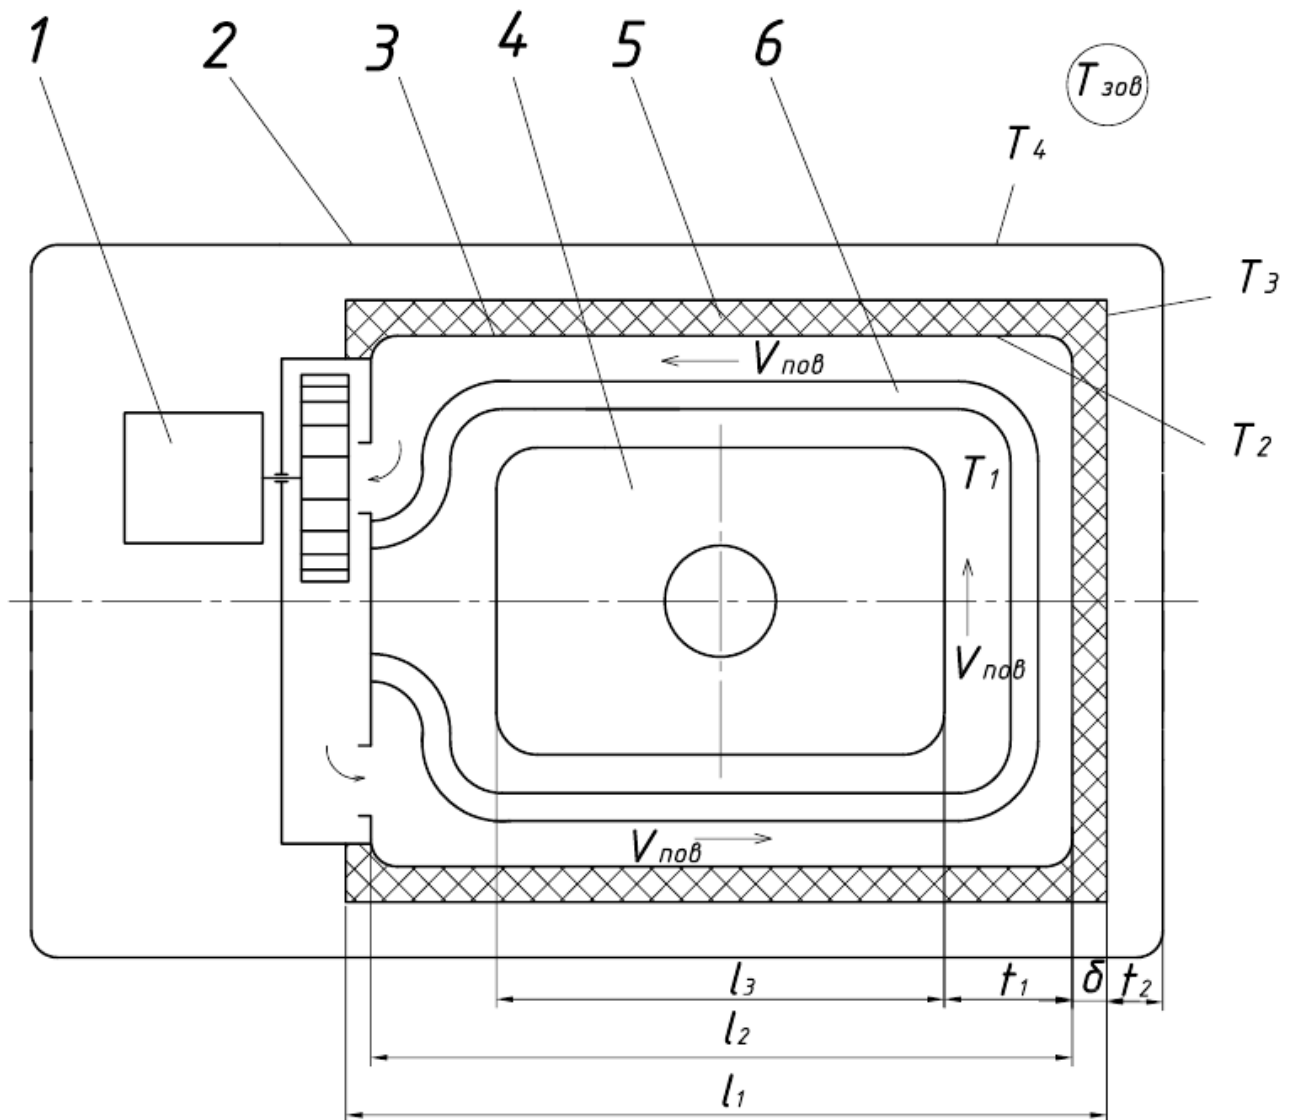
1. Розрахункова схема теплоізоляції хлібопічки: 1 - вентилятор; 2 - зовнішній корпус; 3 - внутрішній корпус; 4 - камера випікання хліба; 5 - термоізоляція; 6 - електронагрівальний елемент; t_1 , t_2 - зазори між стінками кожуху і корпусу; T_1 - температура в камері випічки; T_2 - температура стінки внутрішнього корпусу; T_3 - температура на поверхні теплоізоляції; T_4 - температура стінки зовнішнього корпусу; $T_{зov}$ - температура зовнішнього повітря; $V_{пов}$ - швидкість руху повітря в каналі
